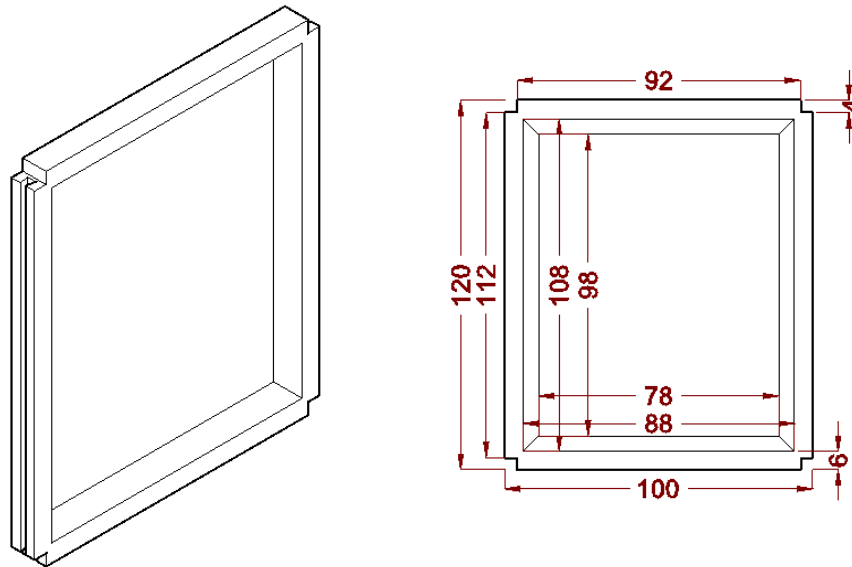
Vista en perspectiva y frontal del diseño propuesto para pieza A (cotas en cm).
